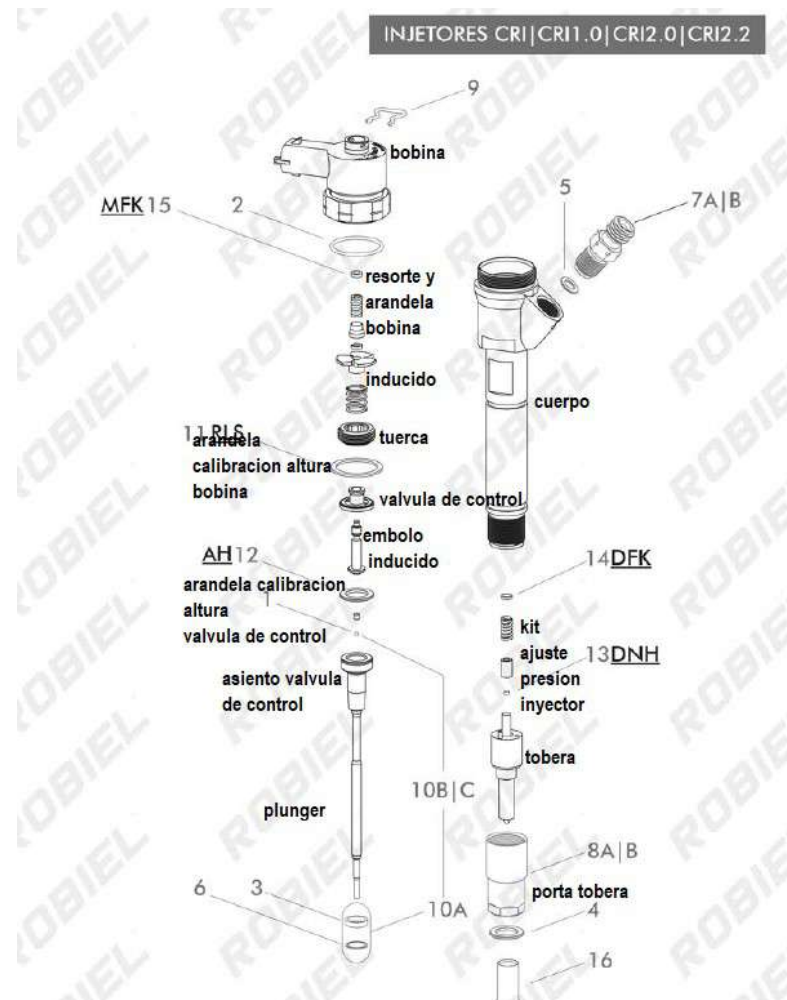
Despiece inyector CRI Bosch. Robiel
